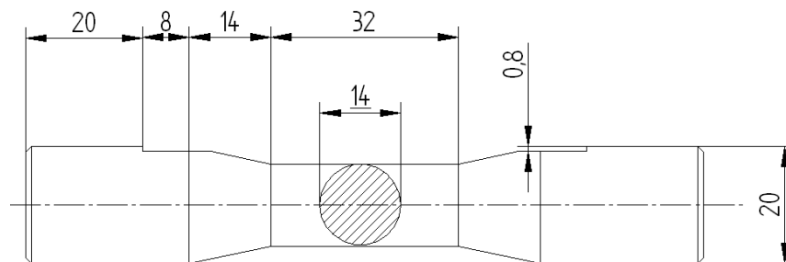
Eprouvette pour essais de fatigue cyclique sur la machine MTS, dimensions en mm.
